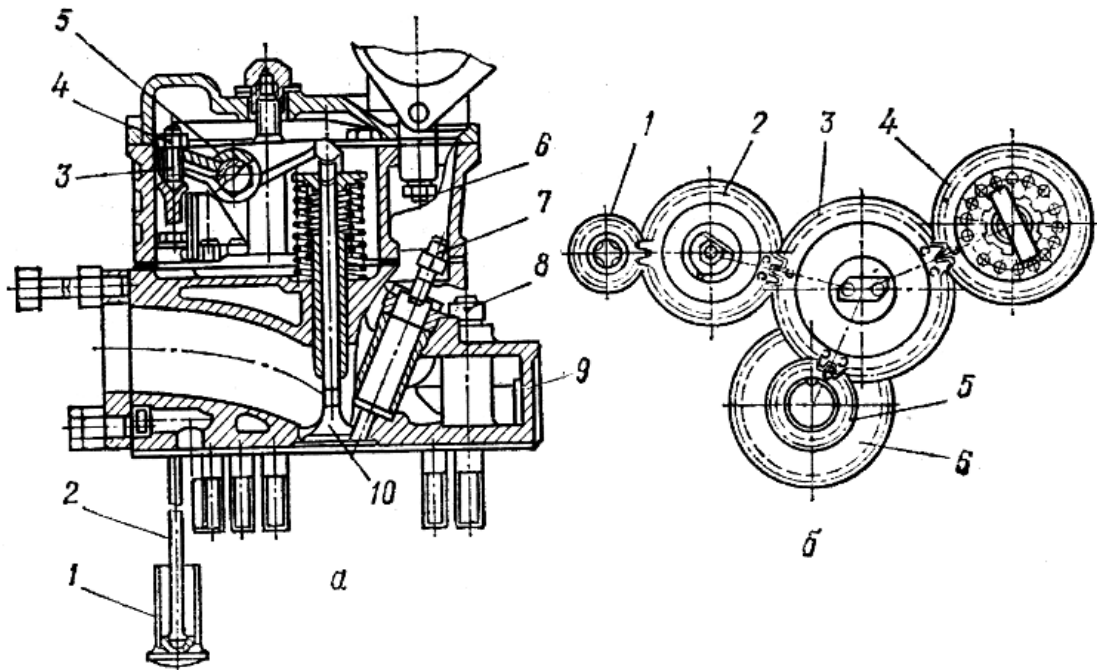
Газораспределительный механизм двигателя Д-240:
